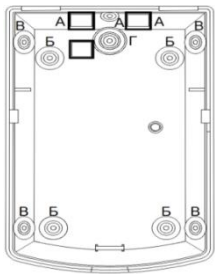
Внешний вид внутренней стороны основания корпуса извещателя с расположением монтажных отверстий и отверстий для ввода проводов
